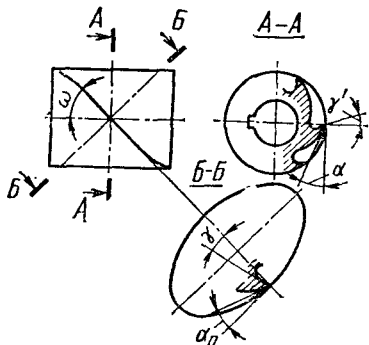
Геометрические элементы режущей части цилиндрической фрезы
